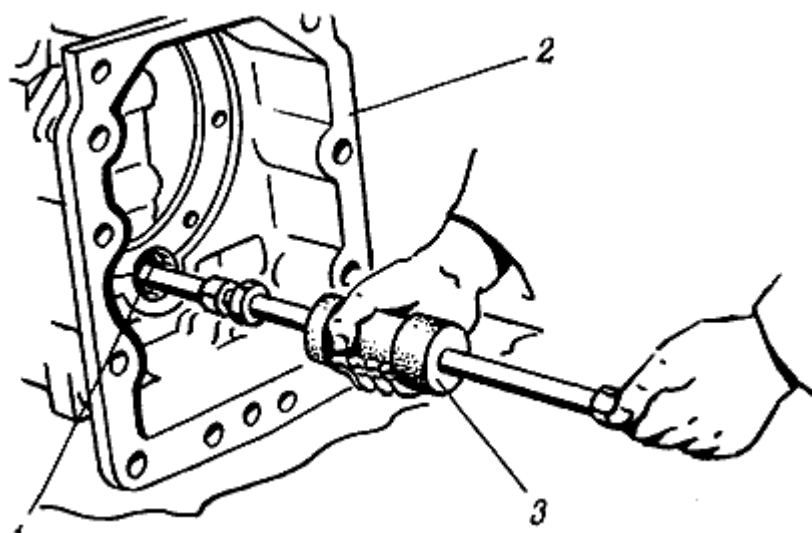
Выпрессовка игольчатого подшипника ведомого вала привода ВОМ:
